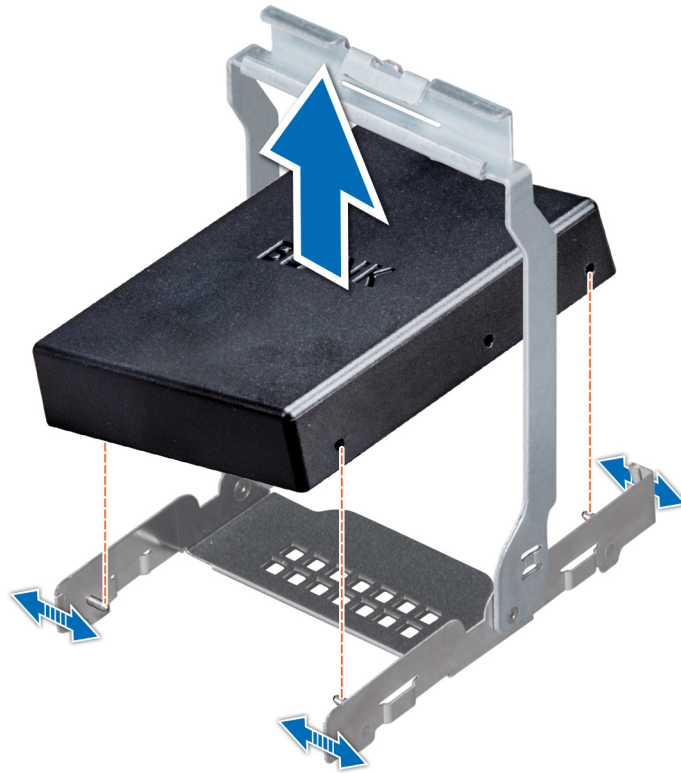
Entfernen des Laufwerksplatzhalters aus dem mittleren Laufwerksträger
